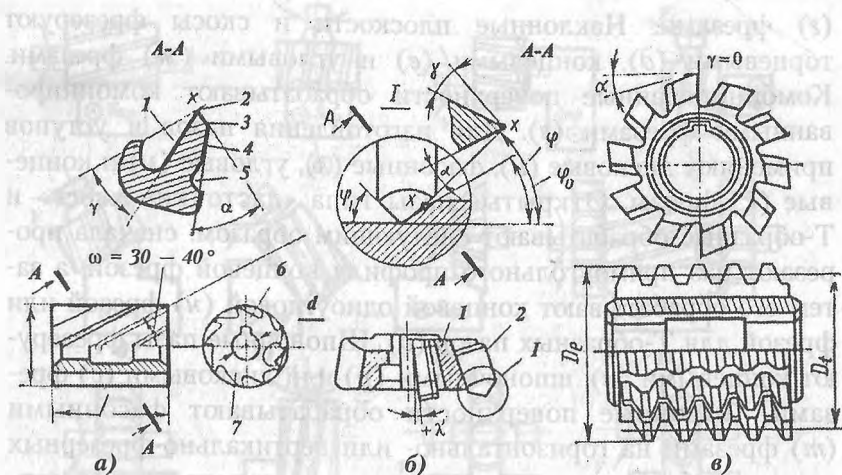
Элементы и геометрия фрез: а — цилиндрических; б — торцевых; в — червячных
